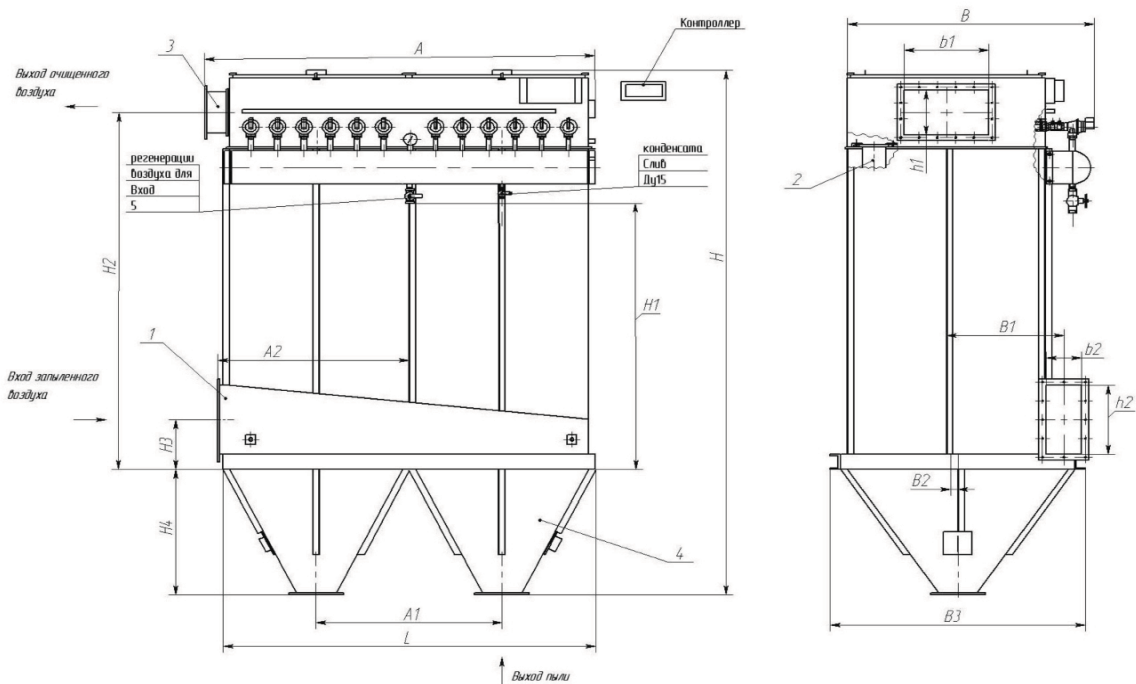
Схема фильтров рукавных типа FRIP-60; FRIP-270; FRIP-360.
